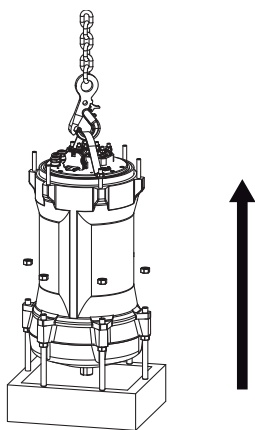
Снятие корпуса двигателя (J 205, J 405)
